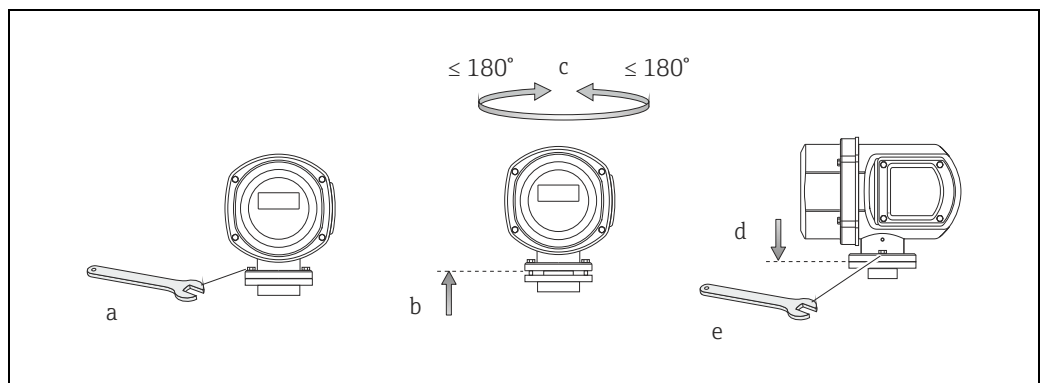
Drehen des Messumformergehäuses (Edelstahl-Feldgehäuse)
